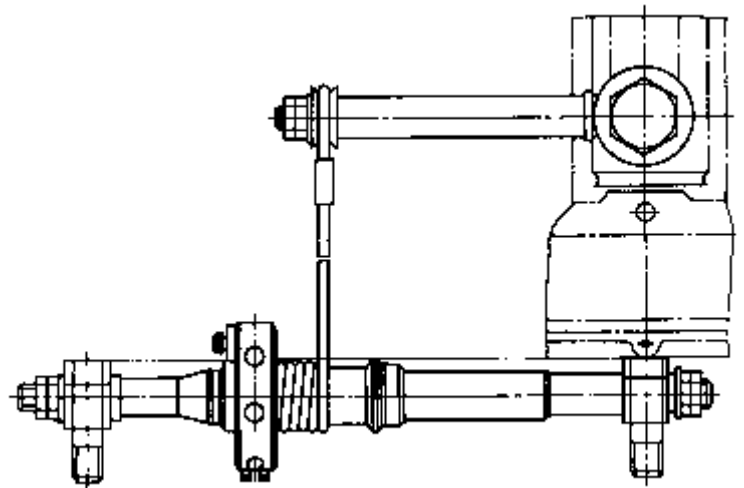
Приспособление для отворачивания гаек коренных подшипников дизеля
